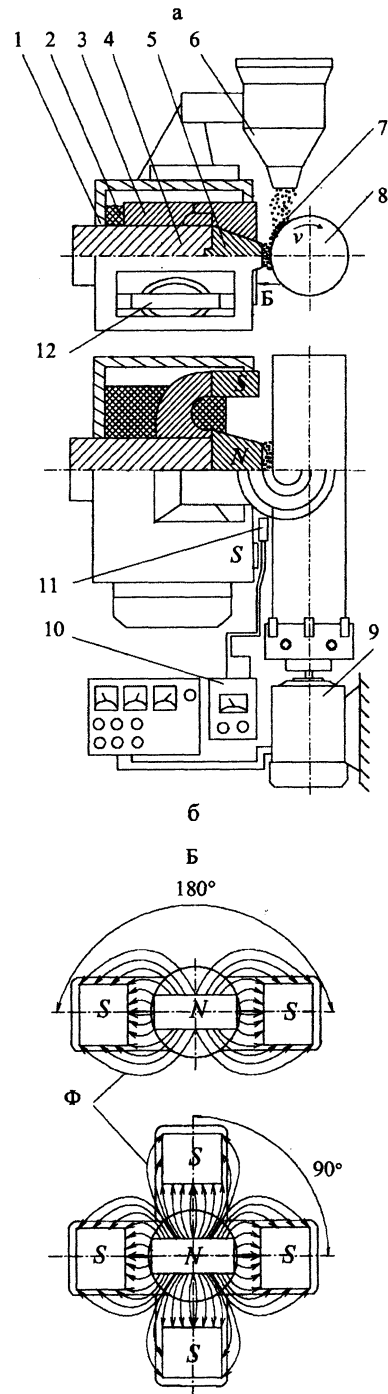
Схемы: а – экспериментальной установки; б – расположения полюсов относительно поверхностей заготовки
